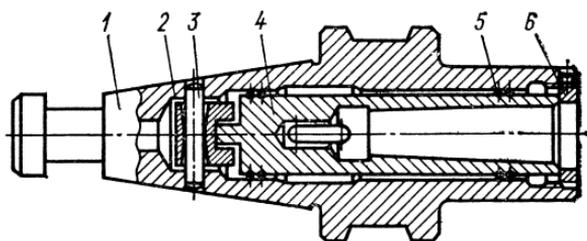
Патрон для крепления разверток фирмы «Шмалькальда»
